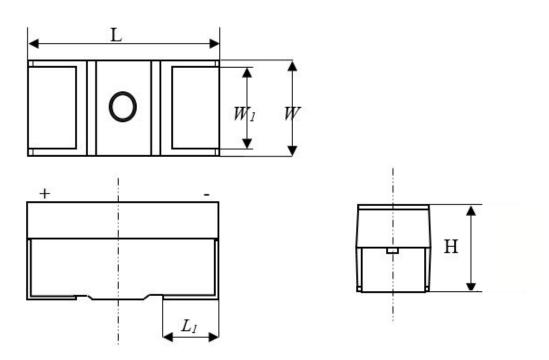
电容器外形尺寸图 表 1 电容器的外形尺寸
